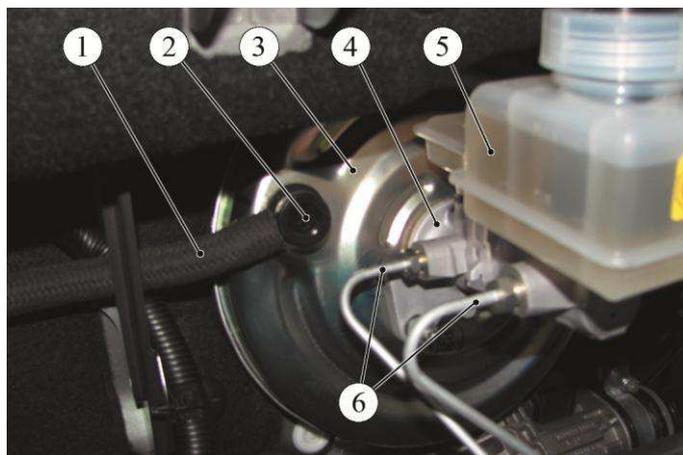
Вакуумный усилитель тормоза в сборе:
